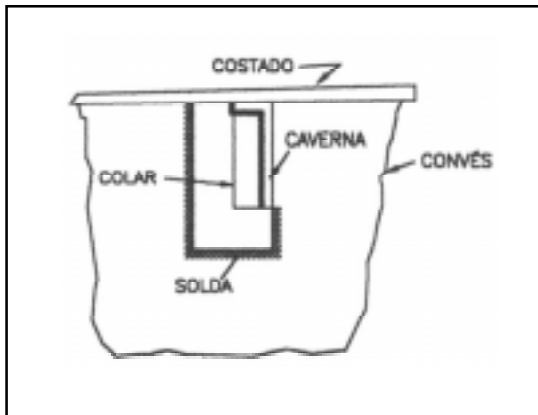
Colar soldado, tornando estanque a passagem de uma caverna no convés
